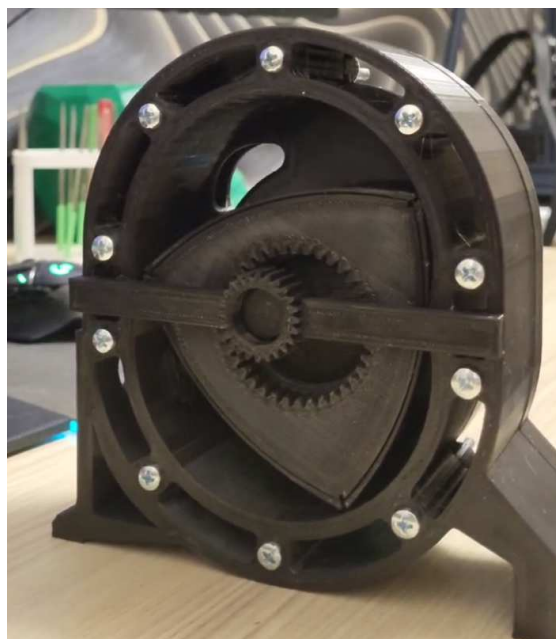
Распечатанная и работоспособная модель роторного двигателя Ванкеля
